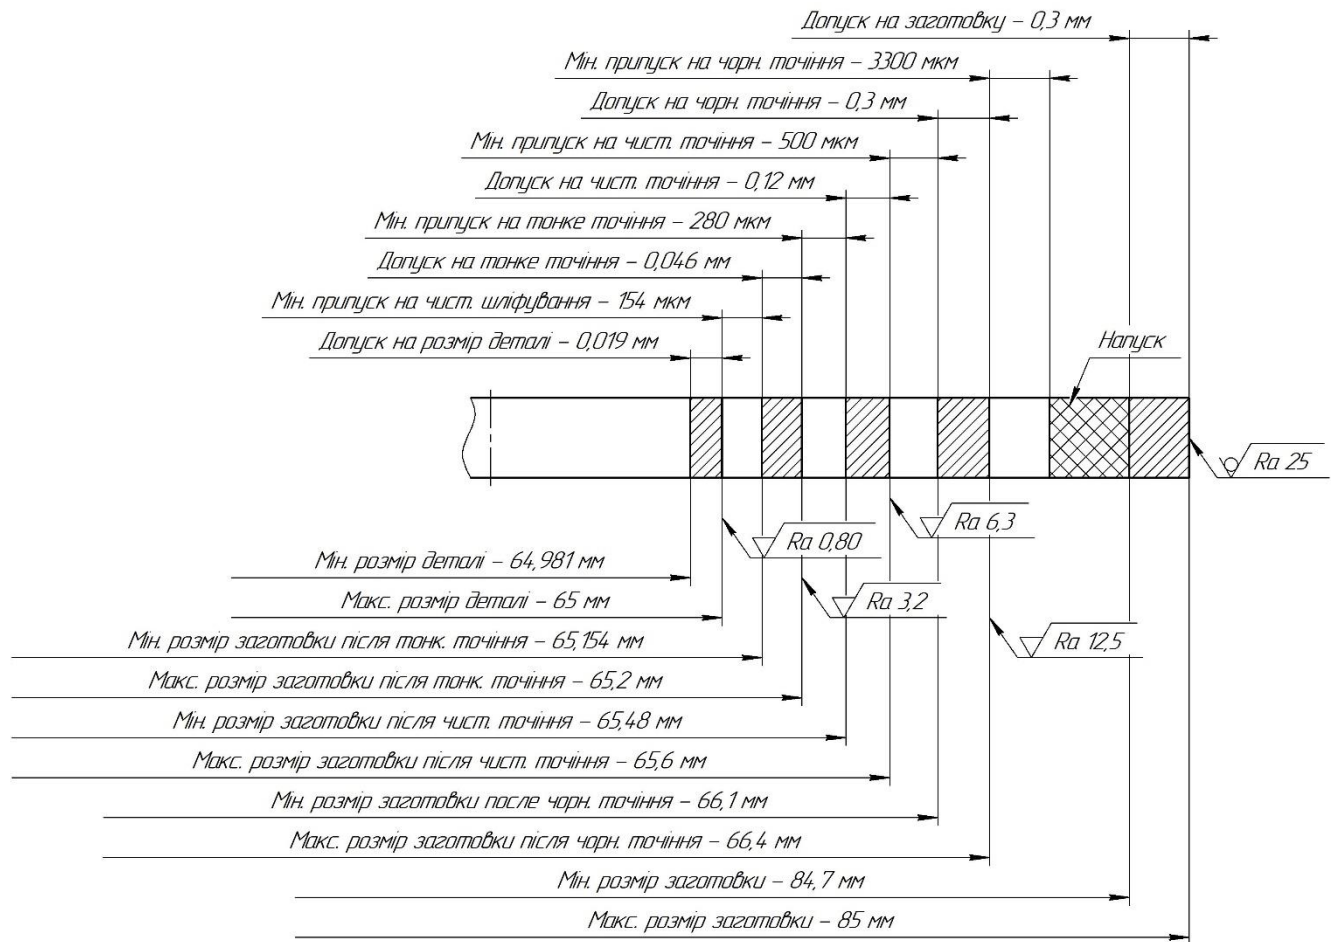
Схема розташування полів припусків та допусків на оброблення зовнішньої циліндричної поверхні діаметром 65h6
